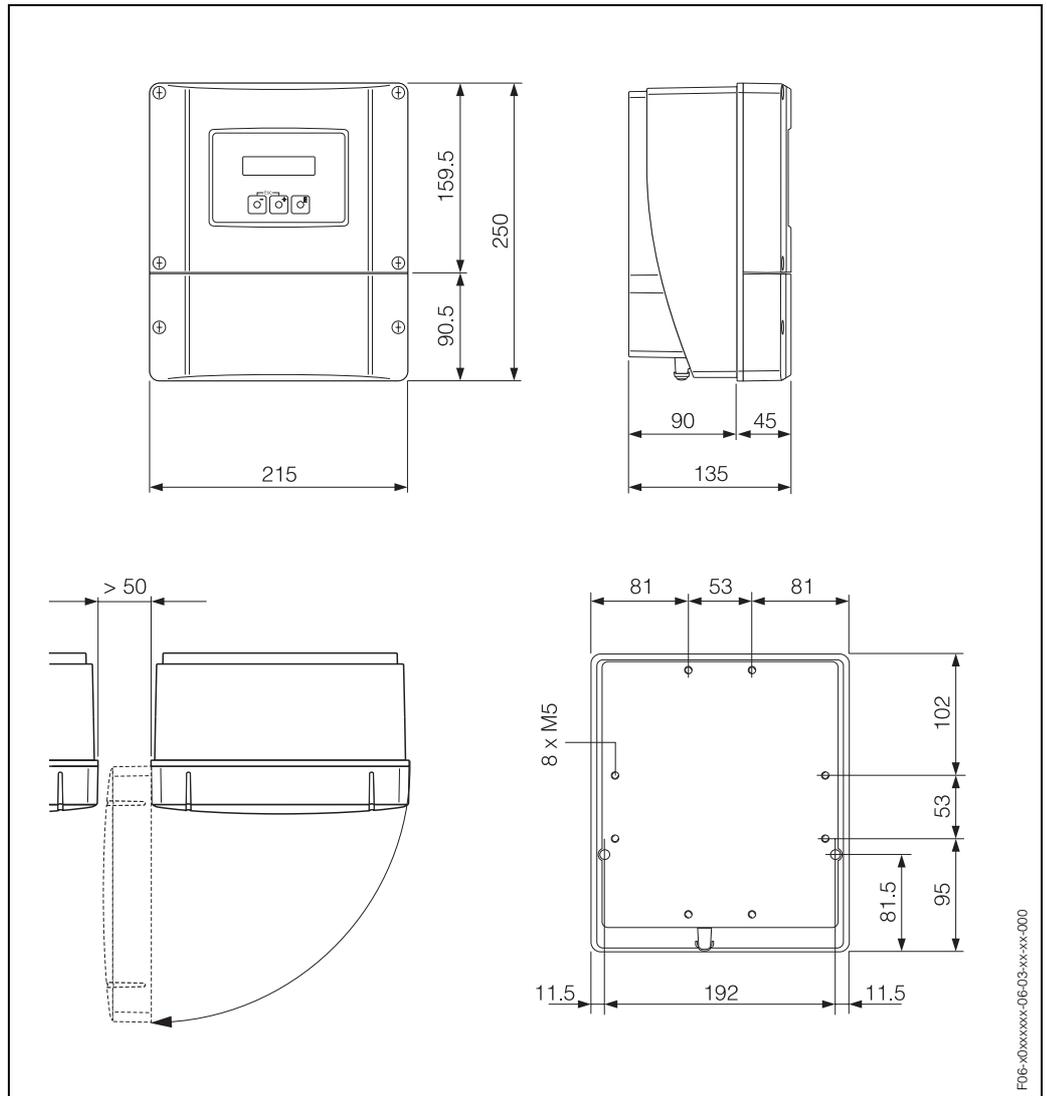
Dimensiones de la caja de montaje mural (montaje en panel y en tubería → Página 33)
